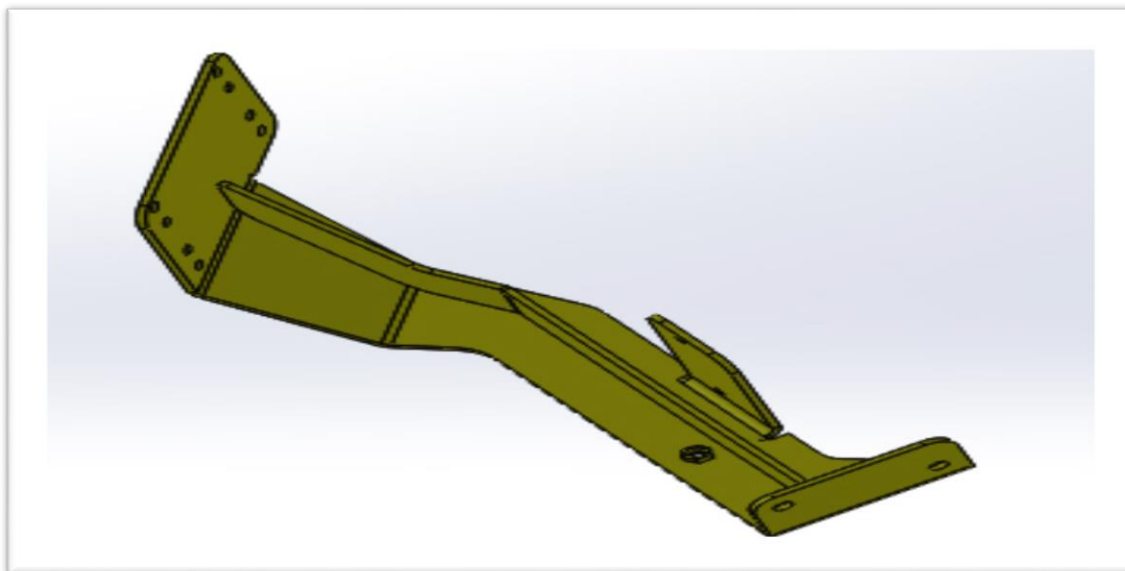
Esboço prévio do componente a ser soldado.
